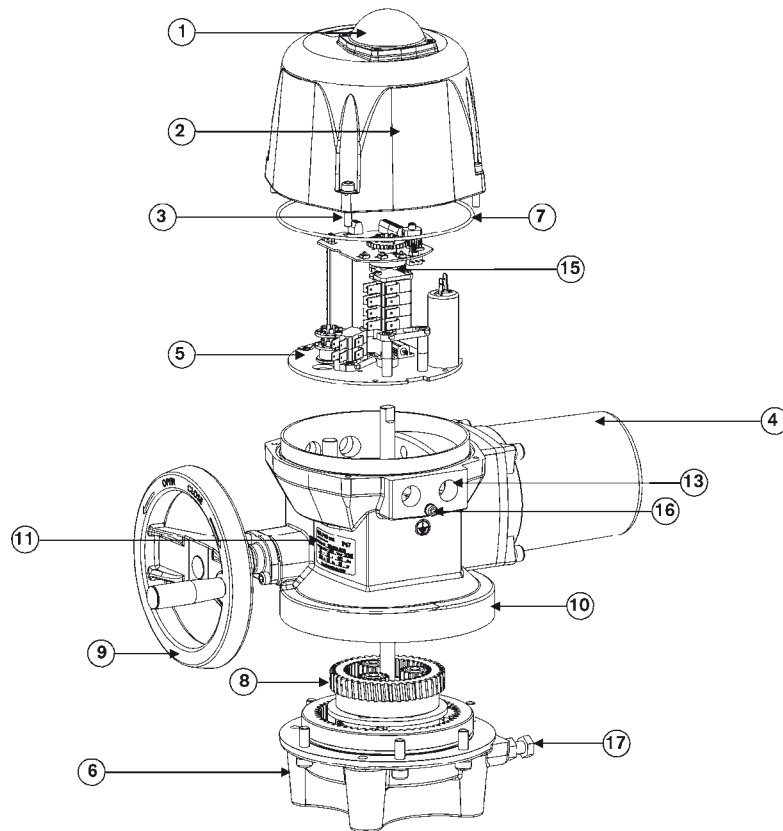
Vue éclatée du moteur 600 - 1 000 Nm
